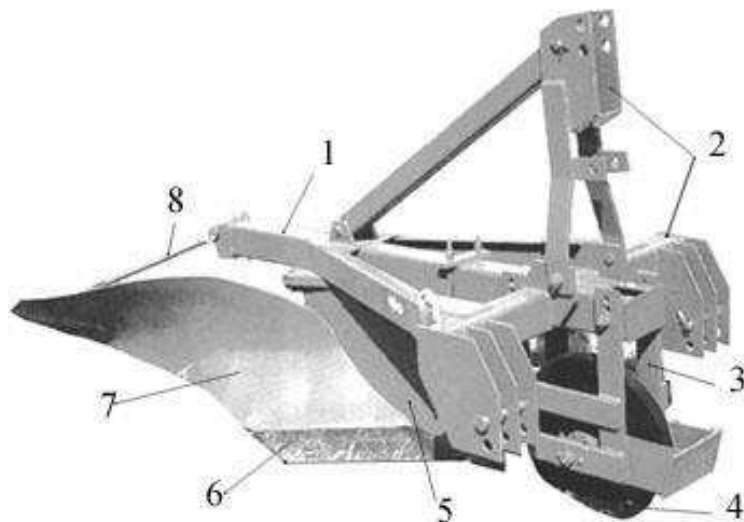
Плуг лесной ПКЛ-70: 1 – рама; 2 – навеска; 3 – кронштейн; 4 – дисковый подрезной нож; 5 – нож корпуса; 6 – лемех; 7 – отвал; 8 – распорка отвалов;
